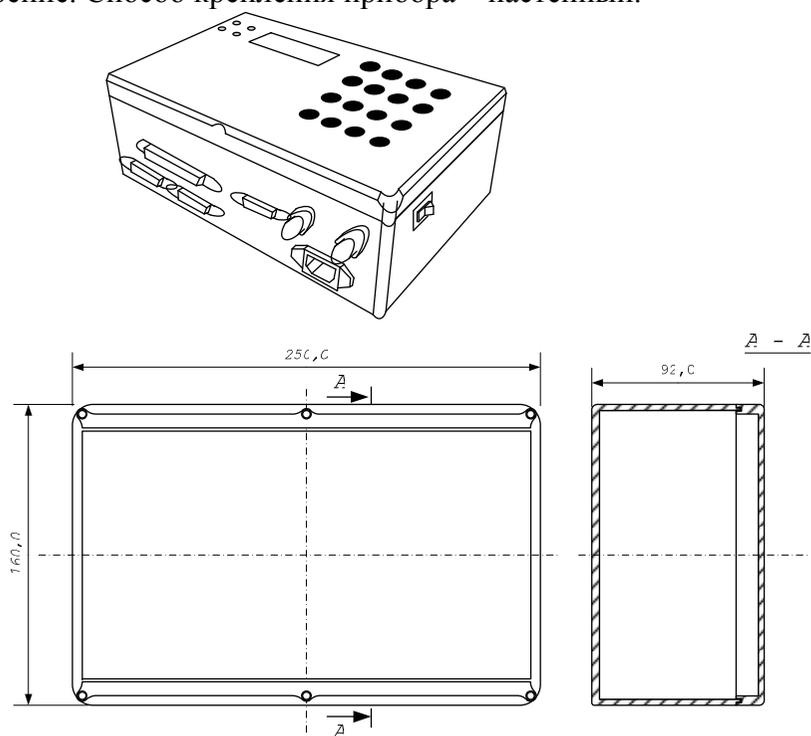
Внешний вид контроллера «БиКуб-РТ23»
